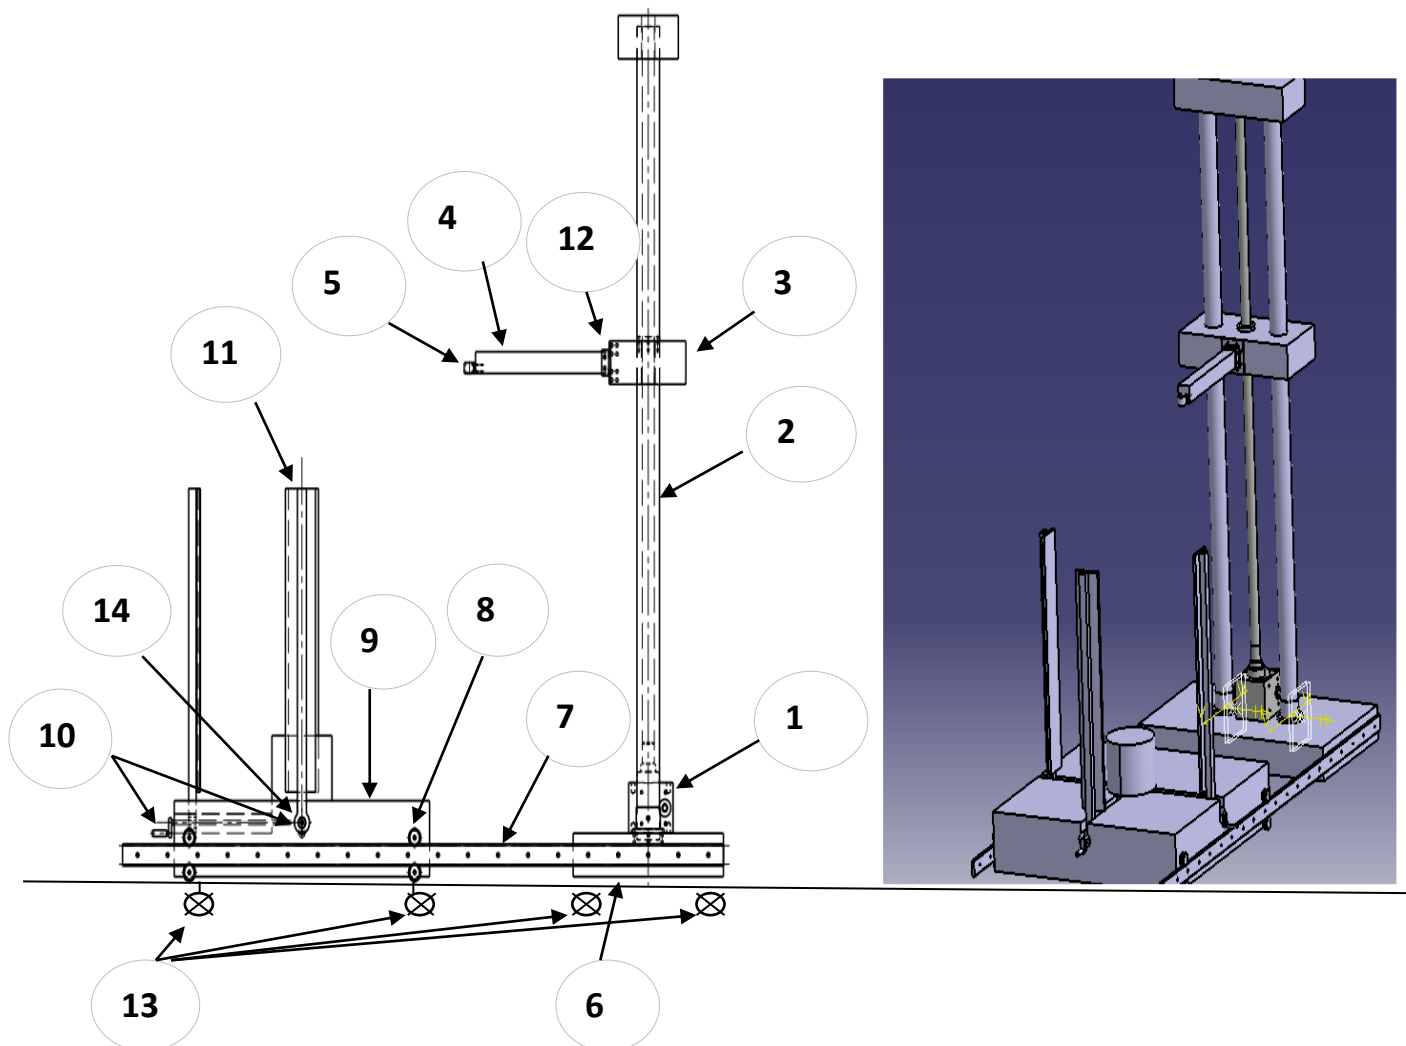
dessin du mécanisme de soudage.
